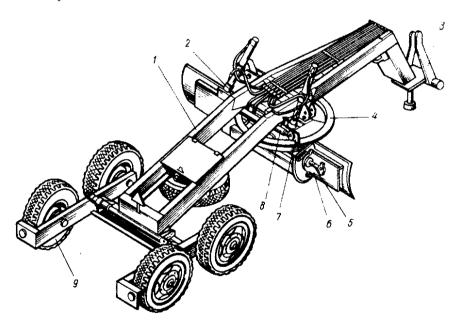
Полуприцепной грейдер без базового трактора: 1, 7 – рамы; 2, 5, 8 – гидроцилиндры; 3 – прицепное устройство; 4 – поворотный круг; 6 – отвал; 9 – задняя ось
